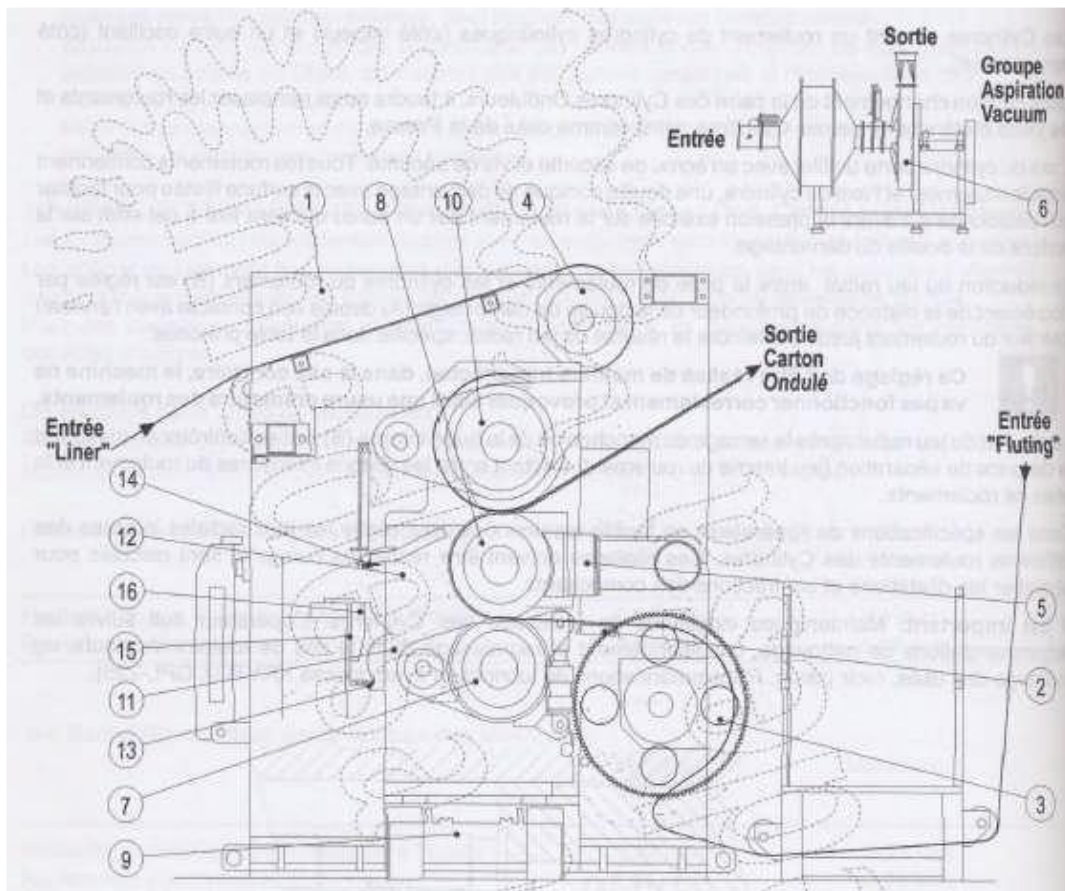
Plan d'ensemble de la machine COM 350. [1]
